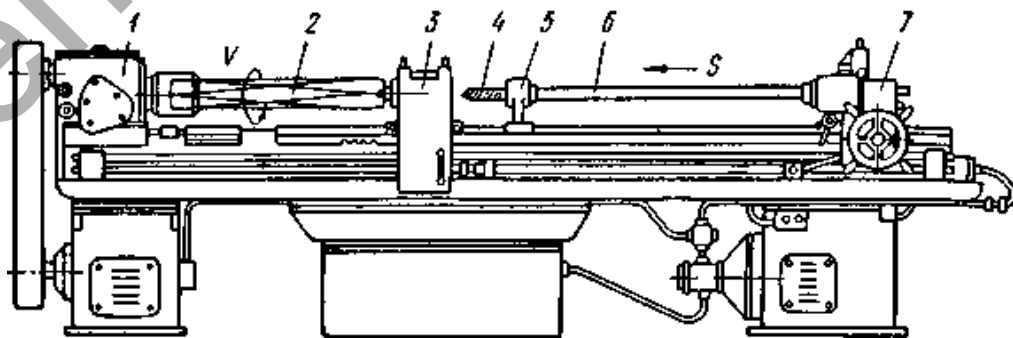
Горизонтально-сверлильный станок для глубокого сверления вращающихся деталей
